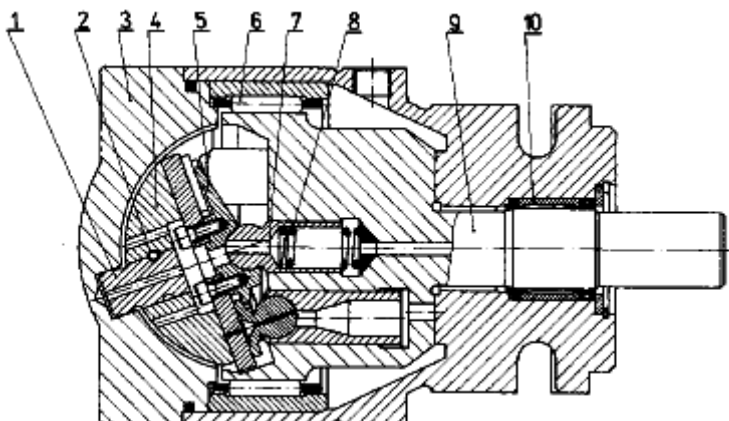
Motor rapid cu pistoane axiale și disc înclinat:
